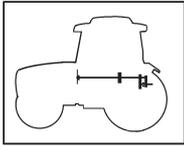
Si nécessaire, pousser en avant le palier de l'arbre arrière et dégager le manchon de raccordement des 2 arbres arrière de la P.d.F..
